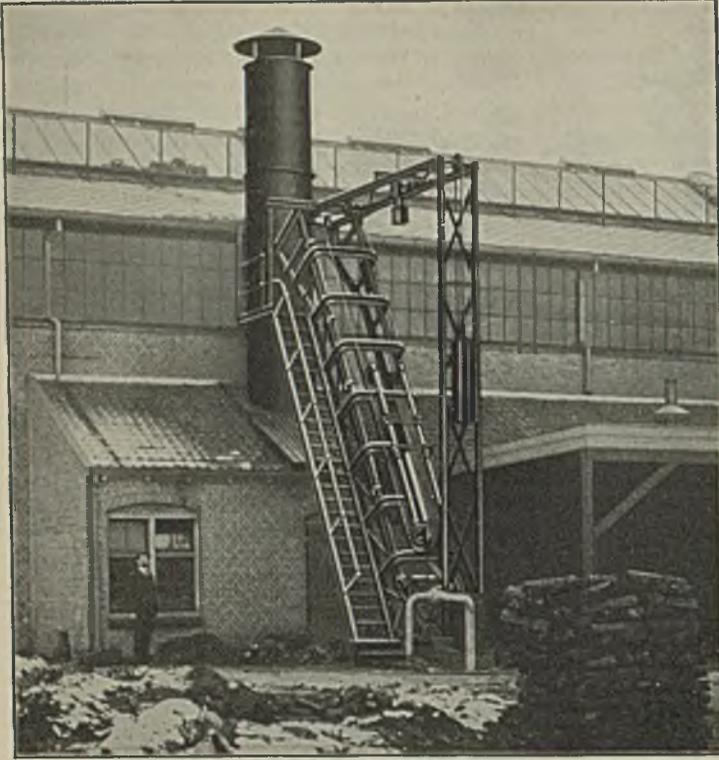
Feststehender, mit Wasserdruck betriebener Schrägaufzug.
